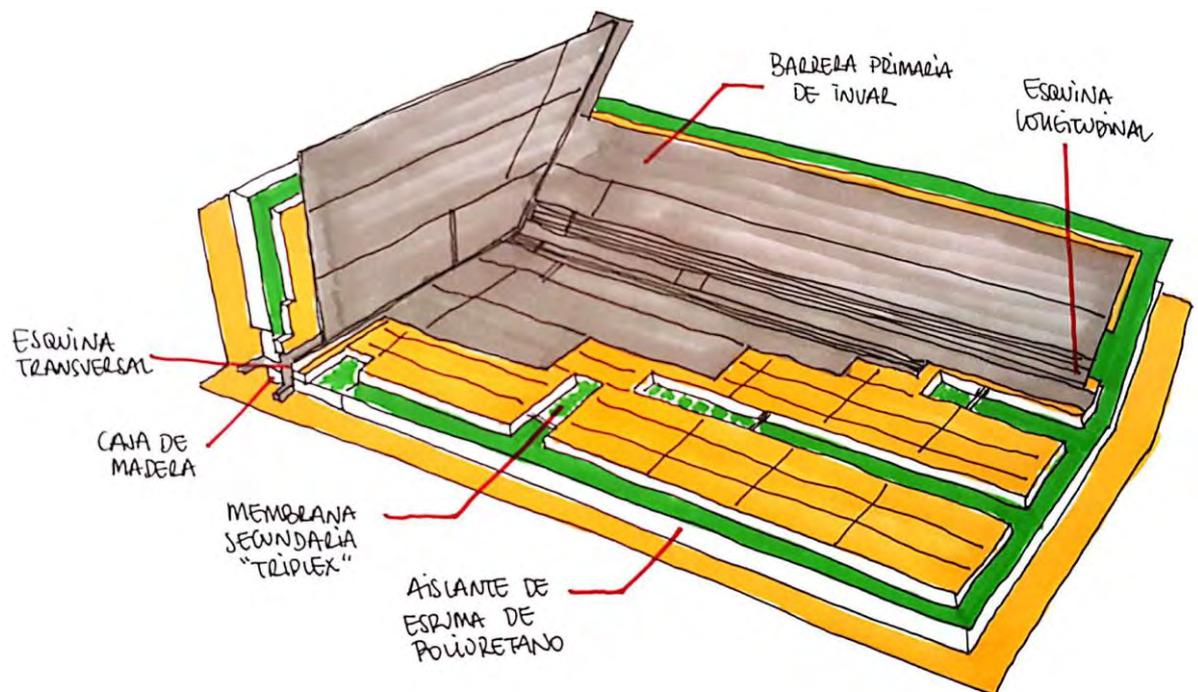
Detalle del interior de un tanque CS1 SIGTTO. Fuente: elaboración propia
